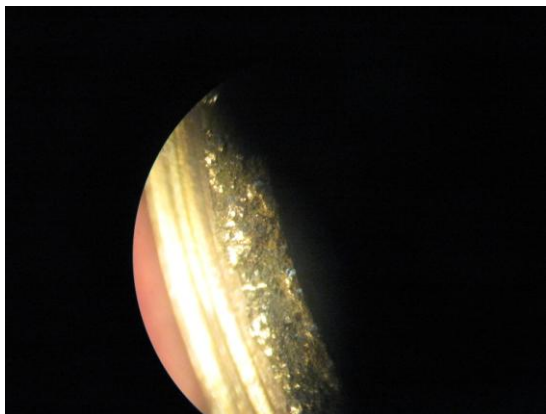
Поверхня злому різьбового з'єднання знімної пробки фільтра з шлаковими та неметалевими включеннями
